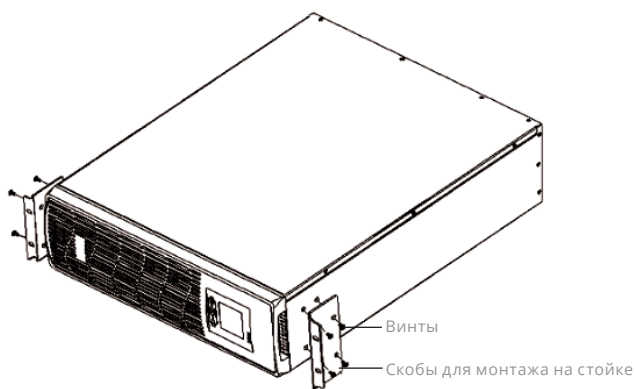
Установка креплений для монтажа в стойку
